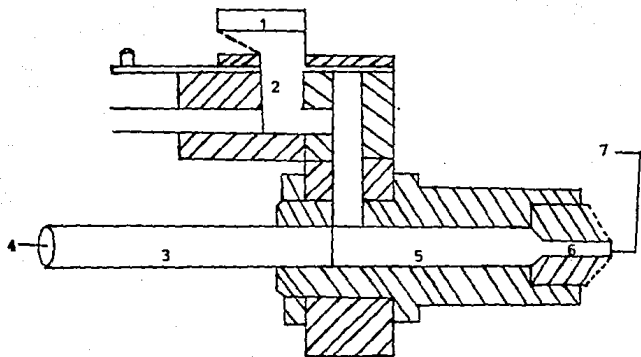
INYECTORA A PISTON. 1.- tolva de alimentacion. 2.- Deposito de resina. 3.- Cilindro hidraulico ( piston ). 4.- Presion hidraulica. 5.- Camara cilindrica de calentamiento. 6.- Boquilla. 7.- Molde.
